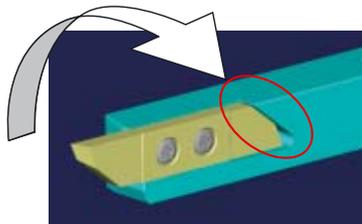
Deux vis de petites sections assurent un maintien parfait de la plaquette sur son support. L'arête de coupe opposée n'appuie pas contre le porte-plaquette et laisse un jeu.
